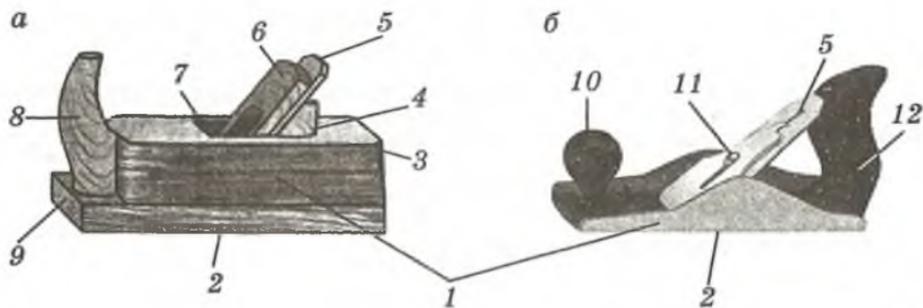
Устройство рубанков: *а* — с деревянной колодкой; *б* — с металлической колодкой: 1 — колодка, 2 — подошва, 3 — пятка, 4 — упор, 5 — нож, 6 — клин, 7 — леток, 8 — рожок, 9 — носок, 10 — ручка, 11 — винт, 12 — рукоятка
